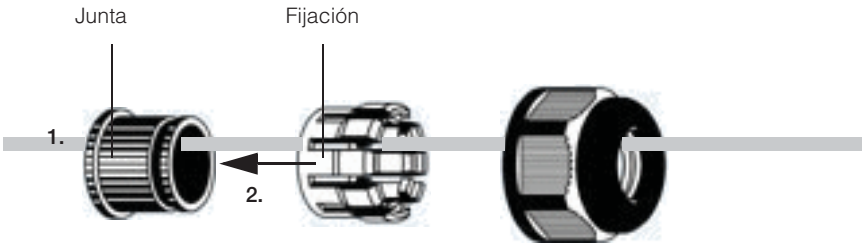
Inserción de los cables en la junta y montaje de la fijación y la junta
